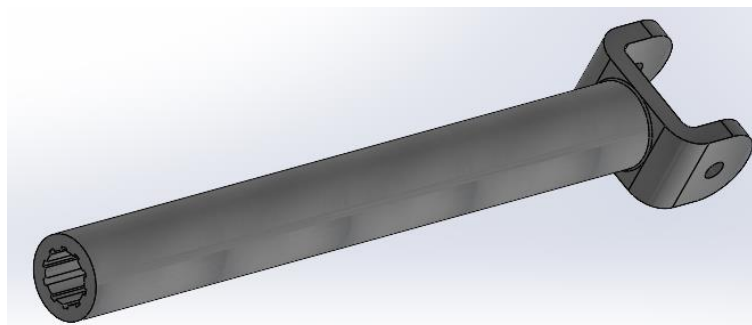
Árbol de transmisión deslizante de la junta cardán en SolidWorks.
